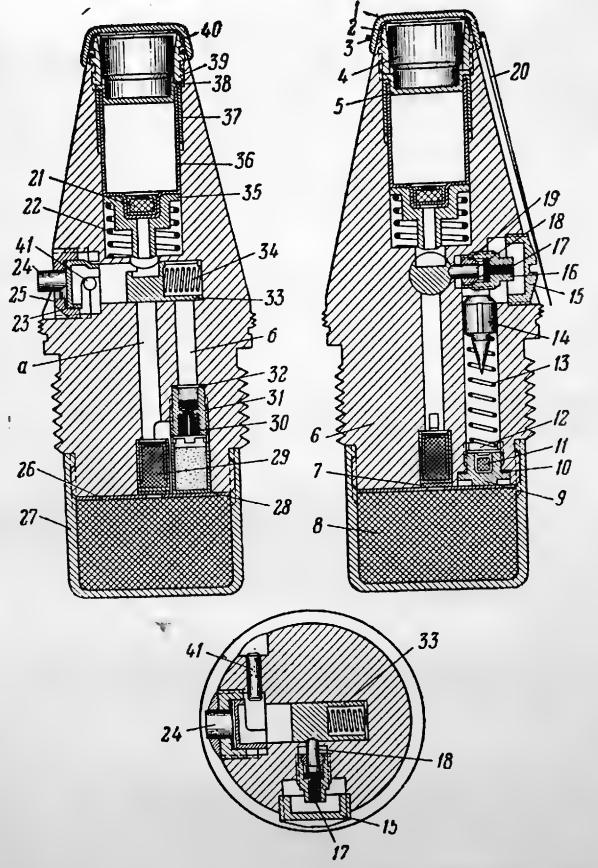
Положение деталей взрывателя ГВМЗ-7 до выстрела (колпак свинчен):
